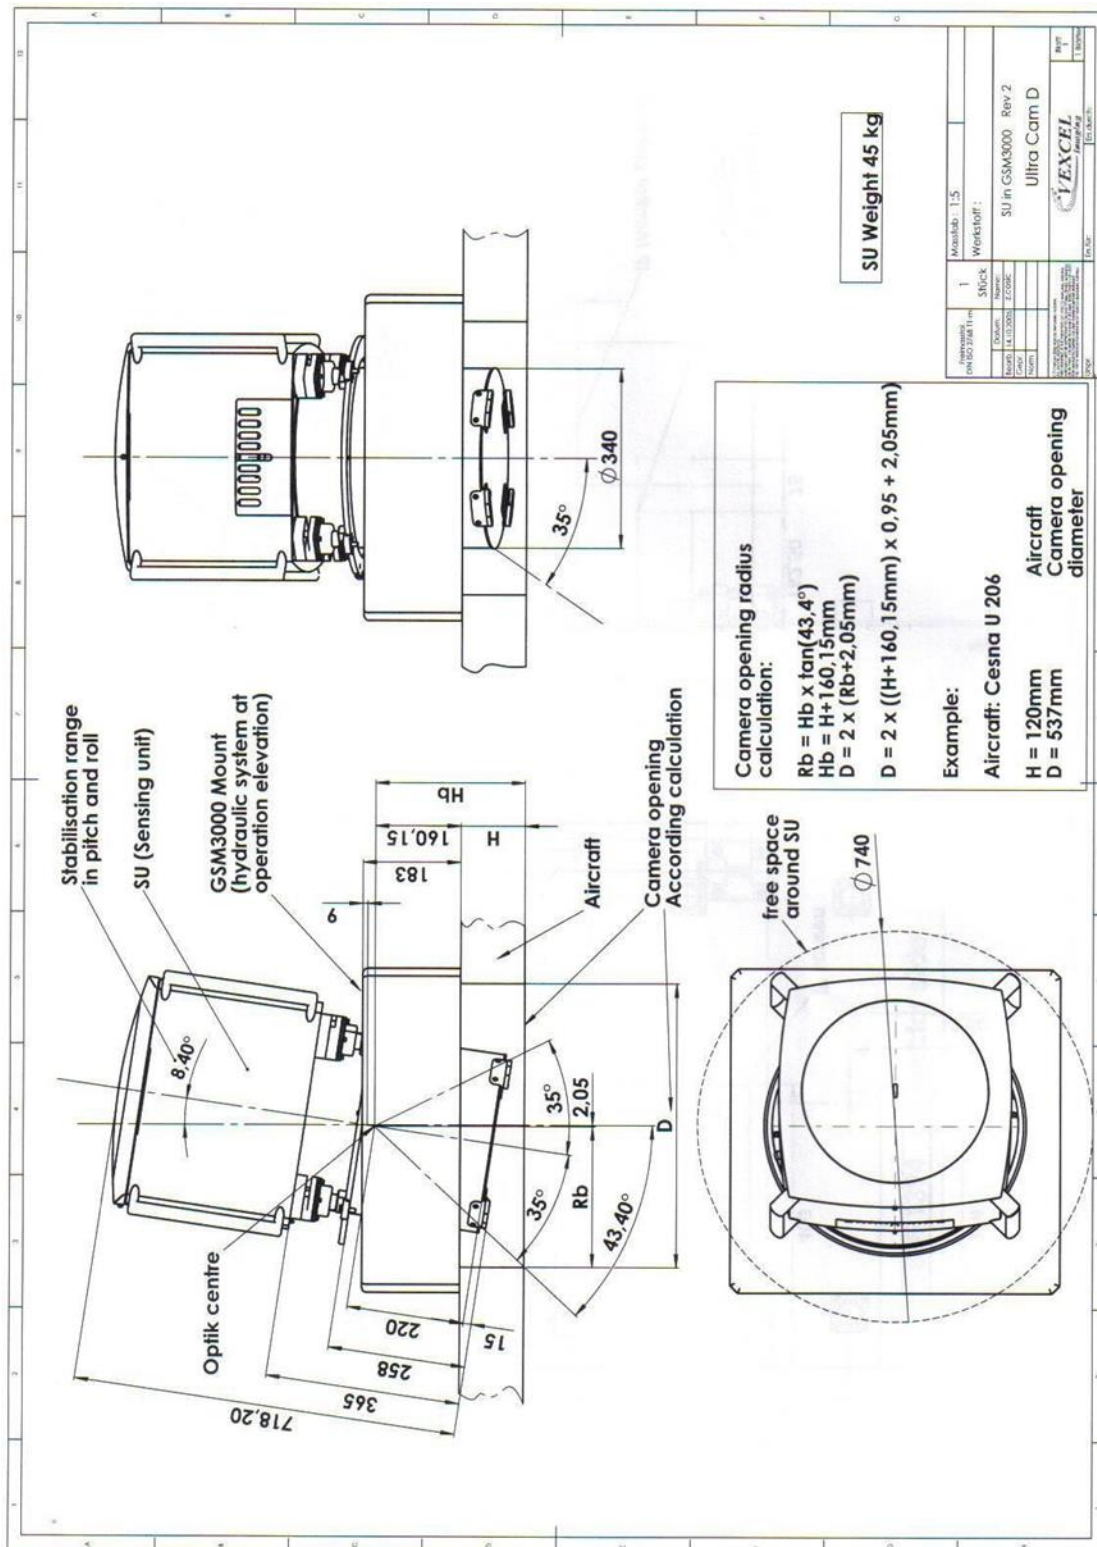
Dimensiones del montaje del SU en la base giro estabilizante GSM3000 (dimensiones en mm)
